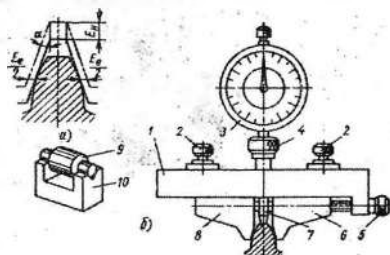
Тангенциальный зубомер: а — схема измерения; б — внешний вид [10, с. 307]
